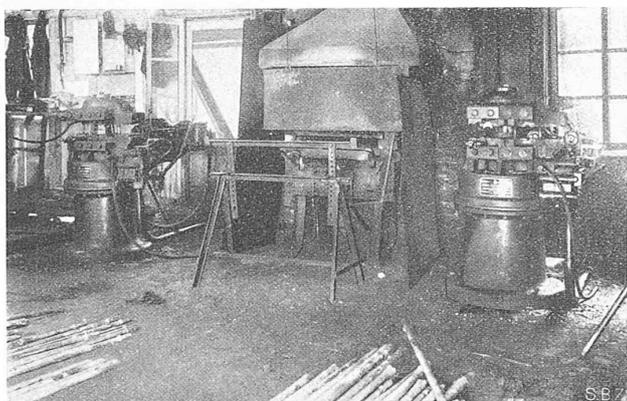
„Ingersoll-Rand“-Bohrer-Schmiedemaschinen.
